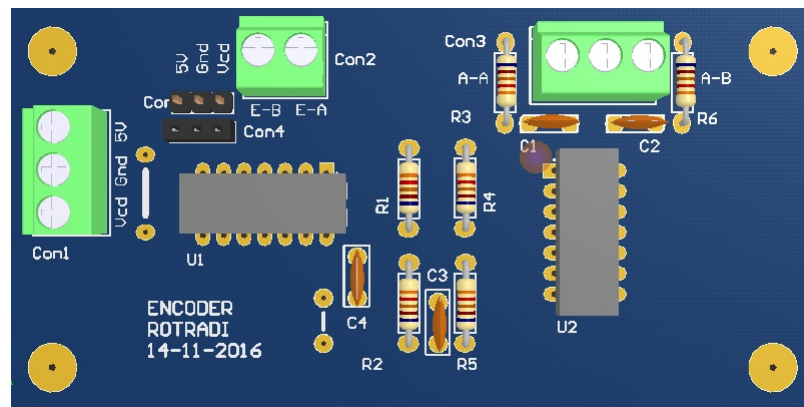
Diseño de PCB para la lectura de la señal del encoder.
